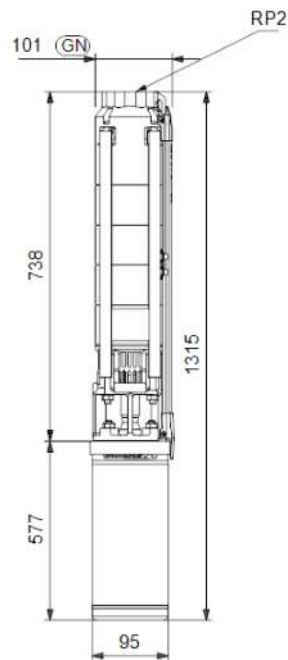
9. Esquema dimensional de la bomba SP 9 -10. Fuente: [33]
